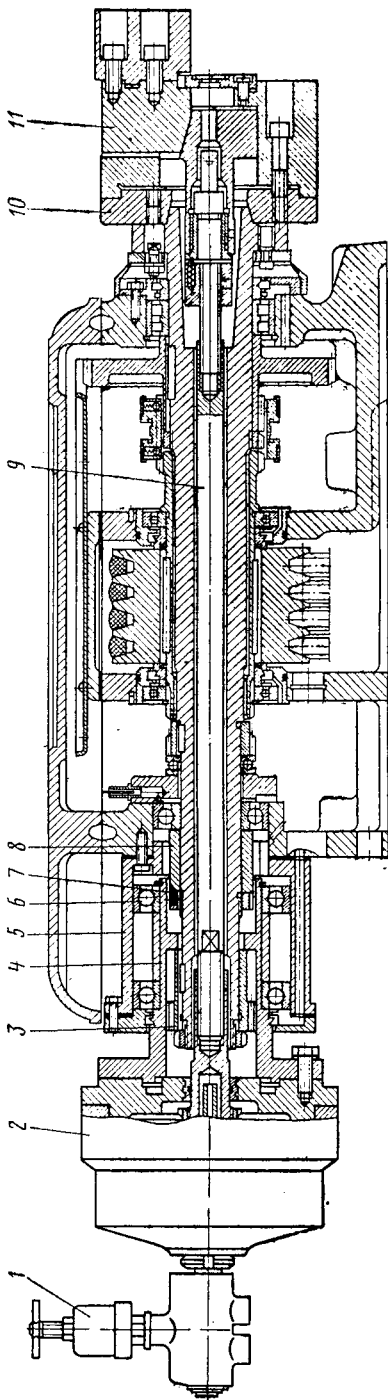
Установка пневмопривода с разгрузкой шпиндельных опор
